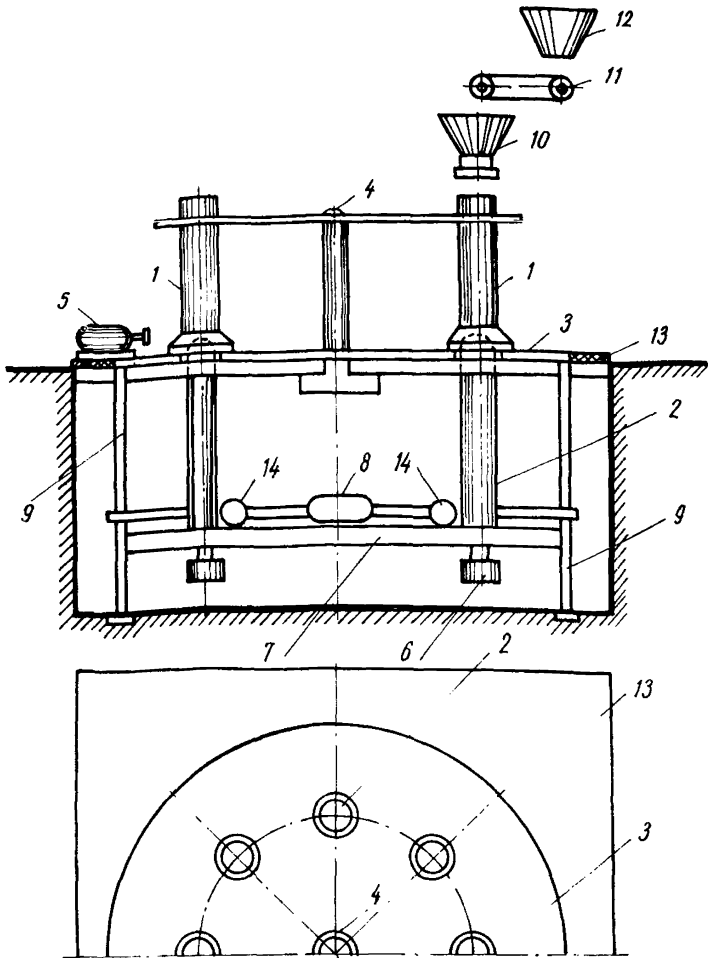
Схема многогнездного станка для изготовления труб способом вибропродавливания
